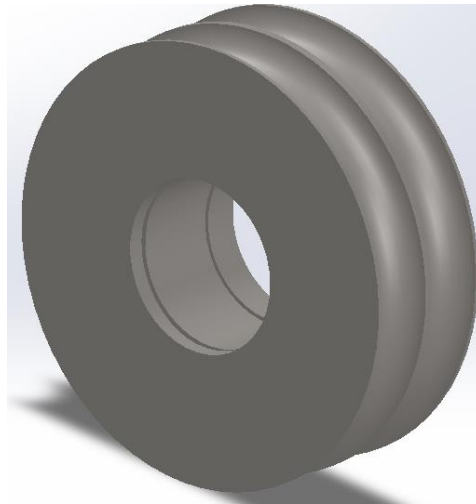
Vista de montaje de pieza N°10 con pieza N°2 (Fuente 99)
